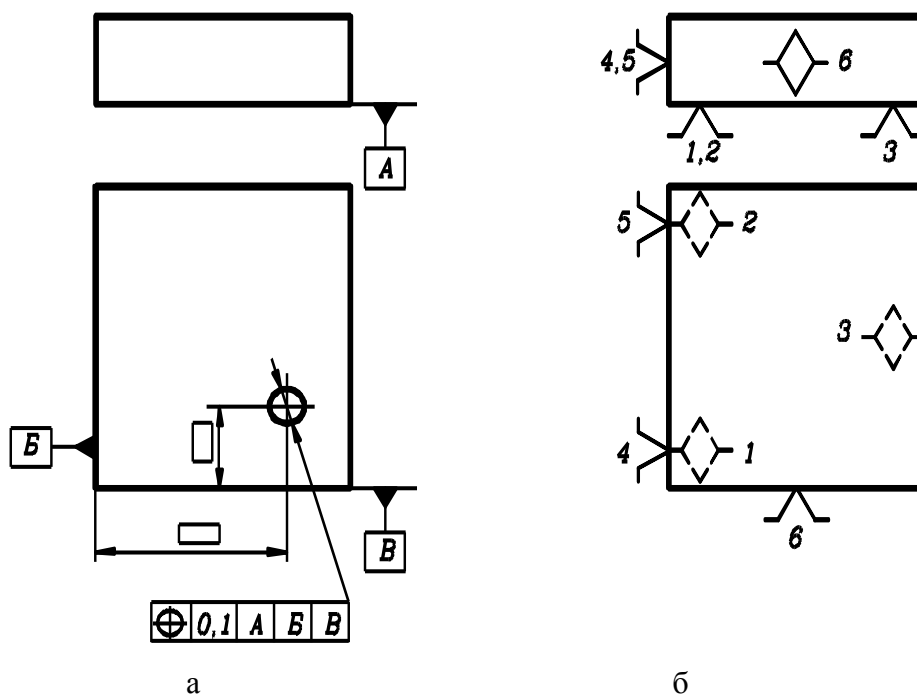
Базирование детали при измерении относительно комплекта баз: а – обозначение измерительных баз на чертеже детали или заготовки по ГОСТ 2.308-79; б – схема базирования детали или заготовки при измерении
